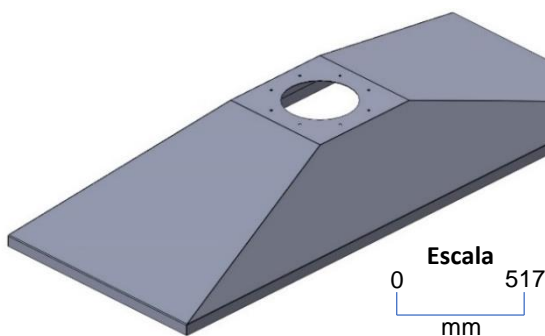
Assembly do CAD das chapas principal e laterais do exaustor.
